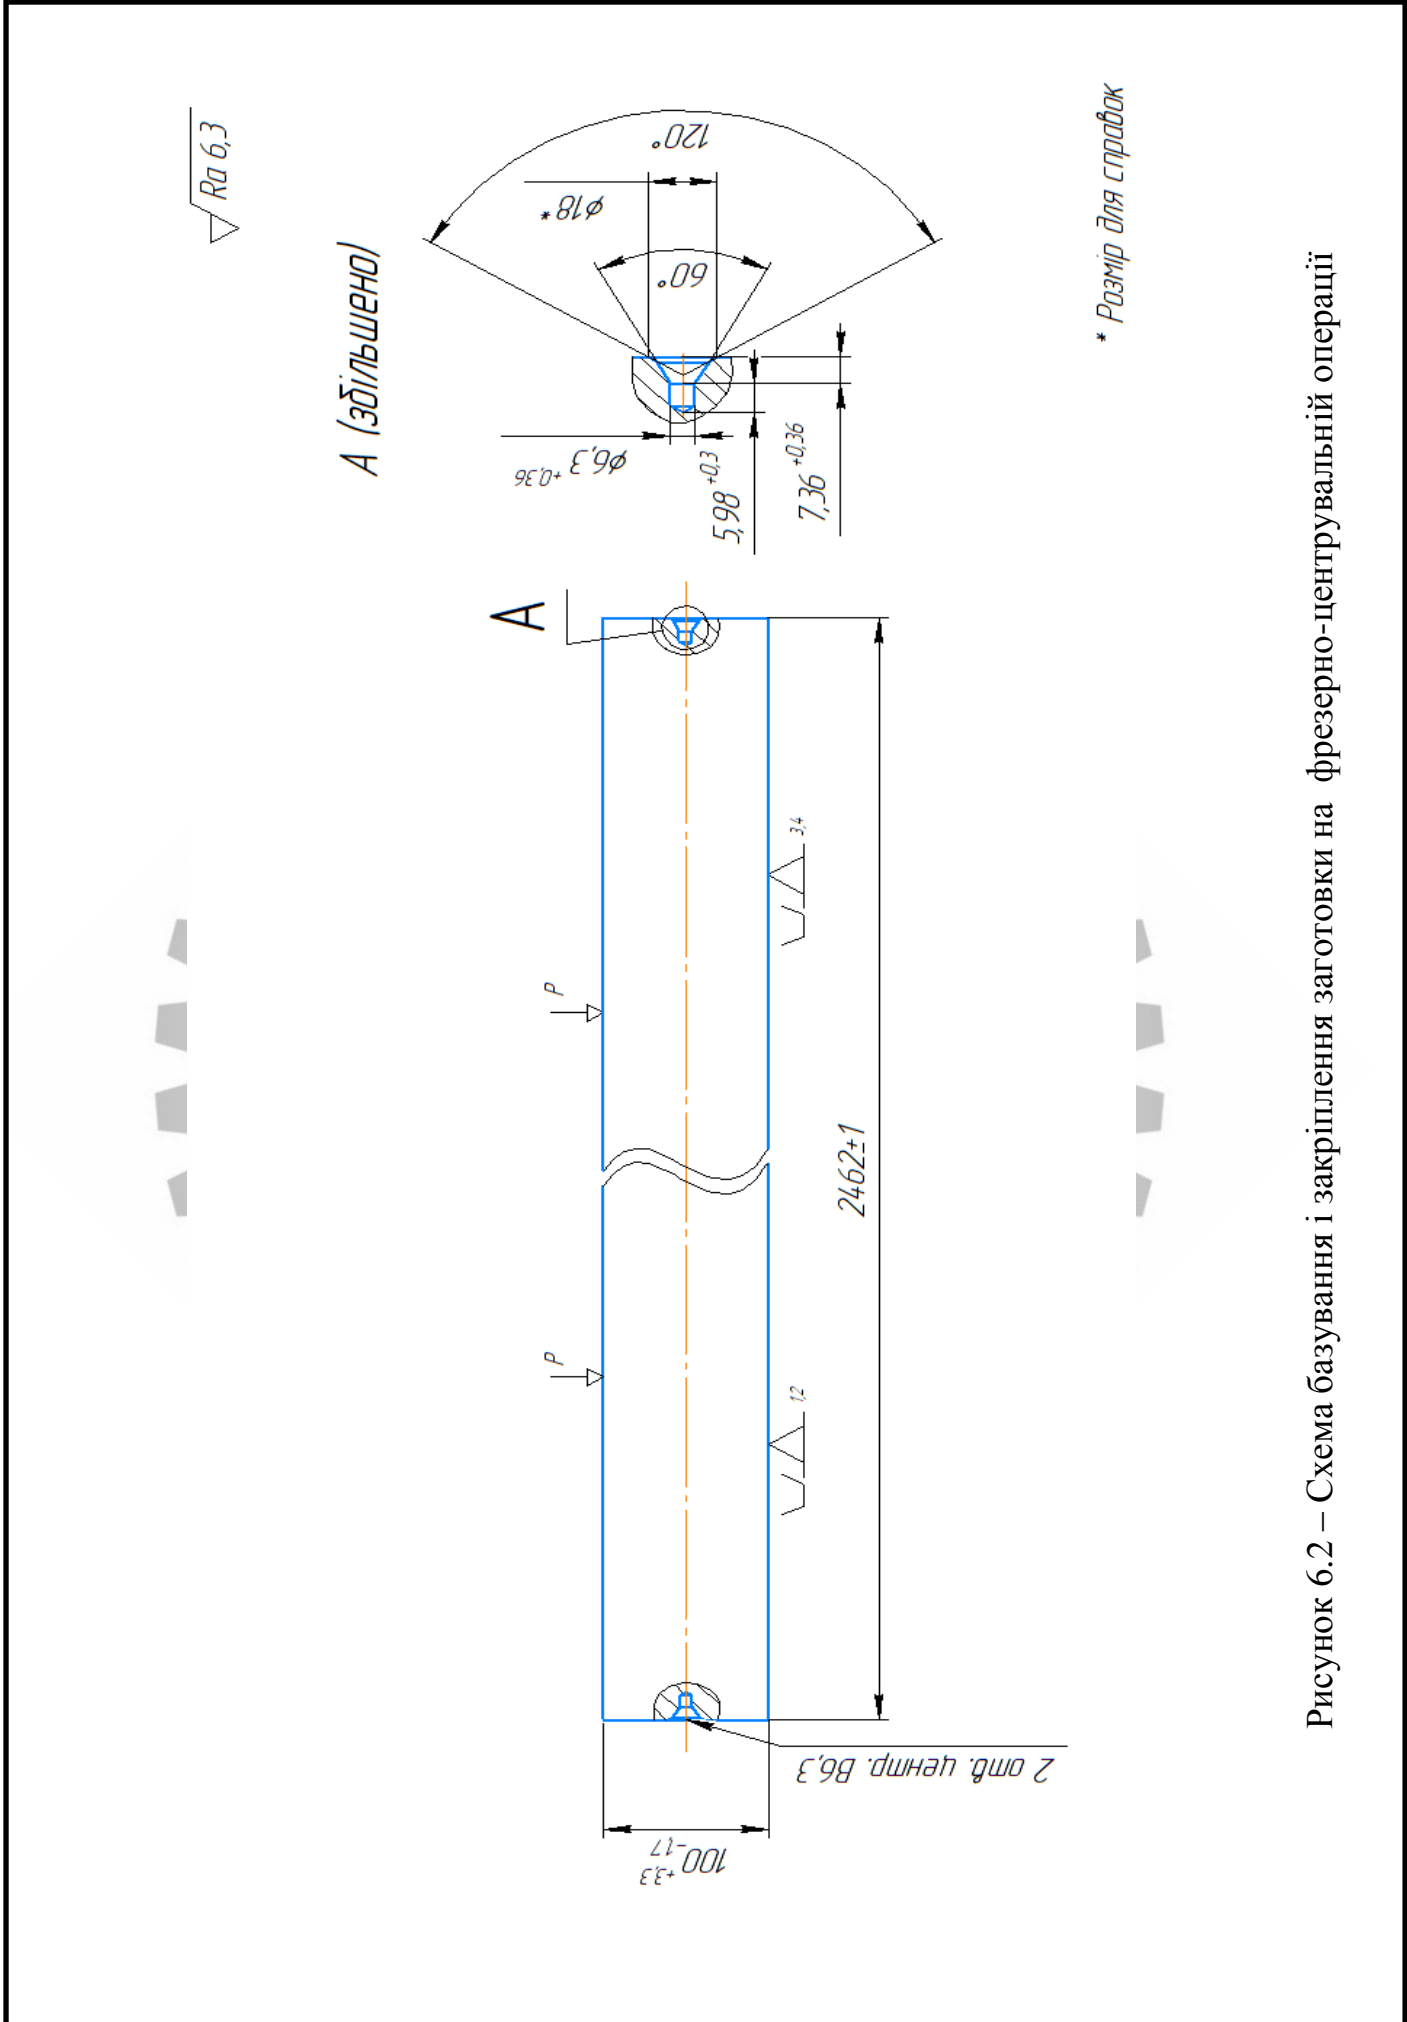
Схема базування і закріплення заготовки на фрезерно-центральної операції
